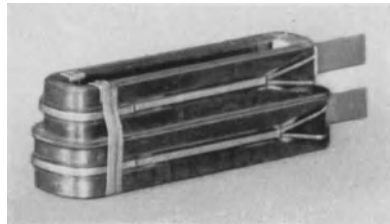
Wendepolspule aus flachgewickelttem Kupferband (Werkbild Siemens).
